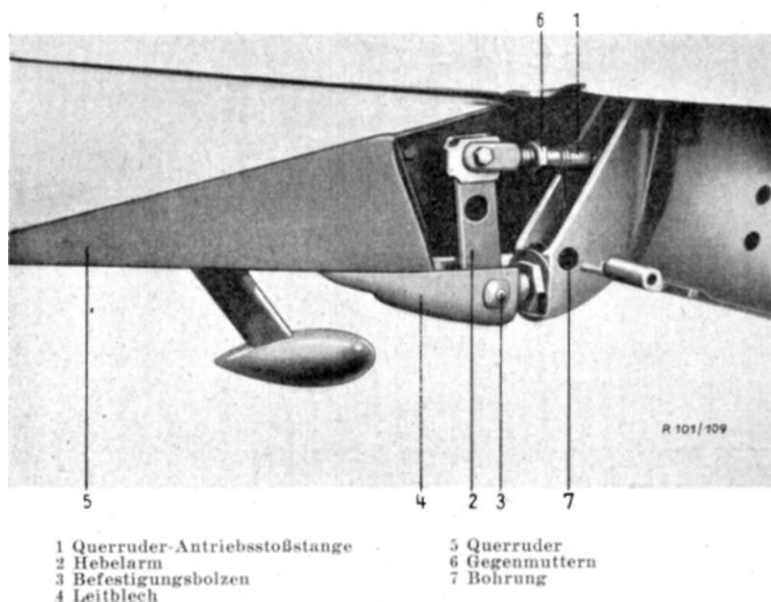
Anschließen der Querruder-Antriebsstoßstange
